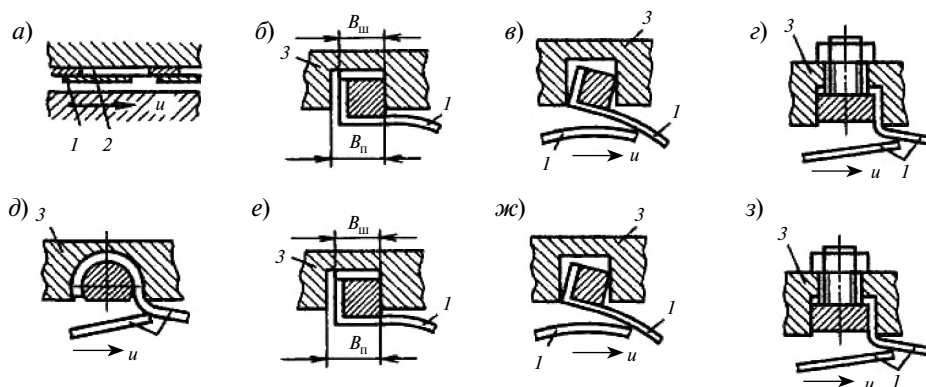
Схемы узла крепления лепестка к корпусу подшипника:
